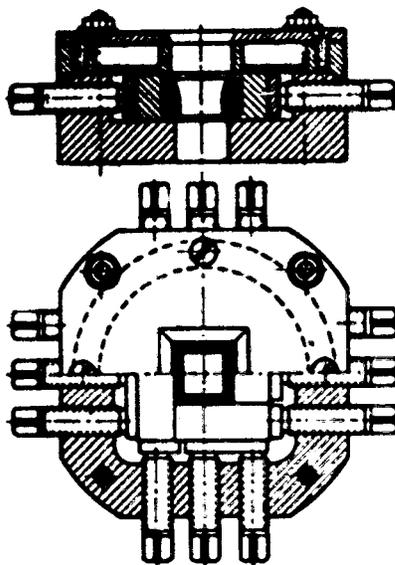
Verstellbares rechteckiges Ziehwerkzeug
